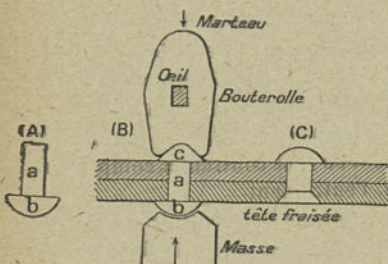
Mise en place d'un rivet pour assembler deux plaques de tôle.
